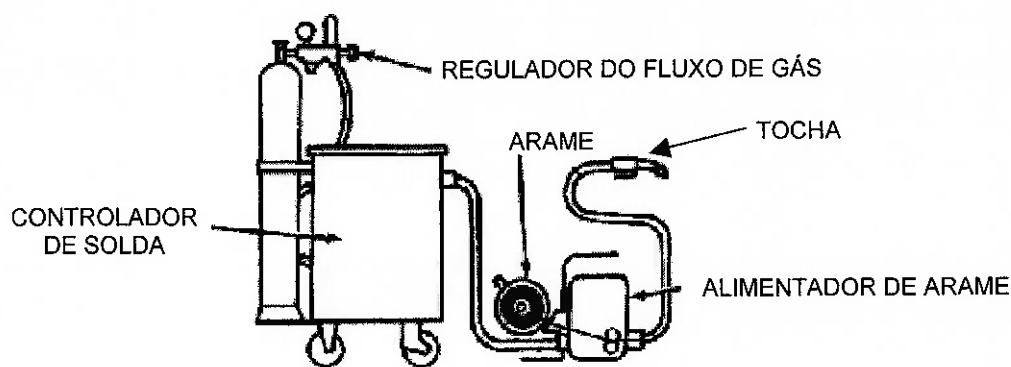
Equipamento Manual de Solda a Arco Elétrico com Proteção Gasosa
